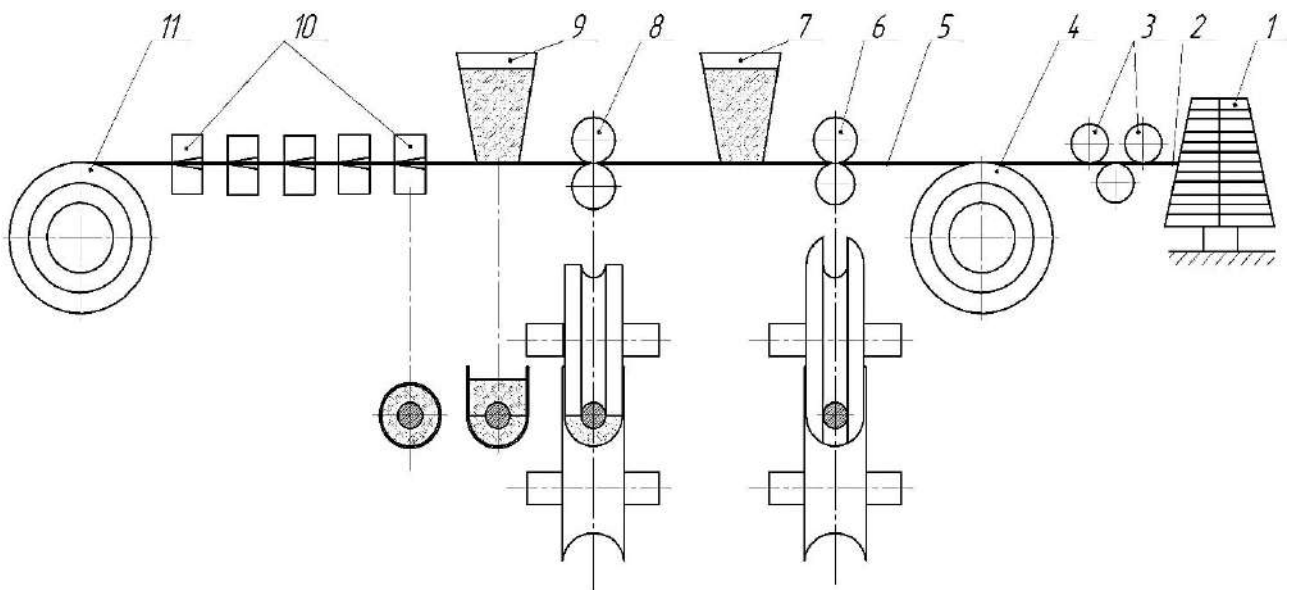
Общий вид технологической схемы изготовления порошковой проволоки
